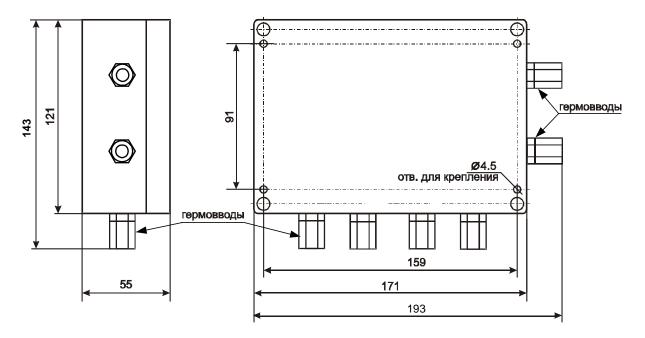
Габаритные и присоединительные размеры КД2 ІР65
